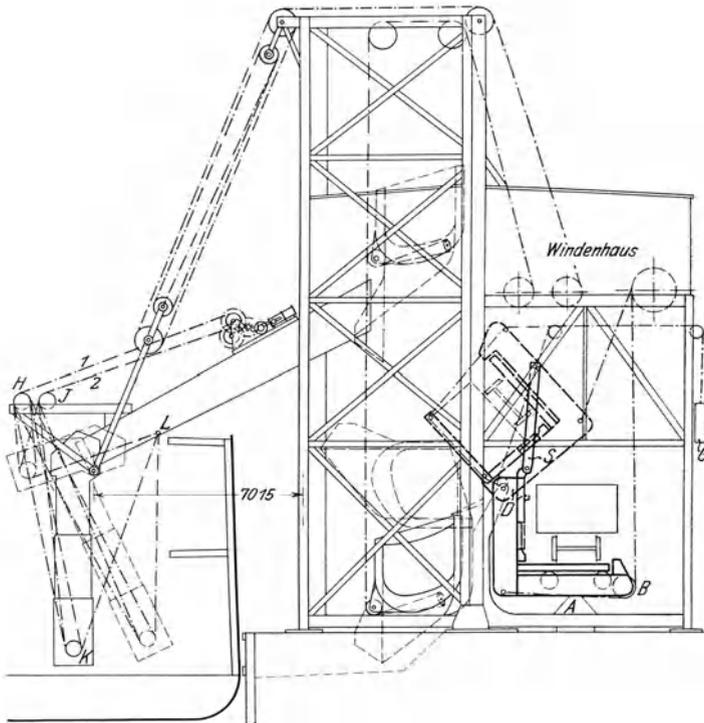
Amerikanischer Seitenkipper für zerbrechliche Kohle mit besonderer Hebevorrichtung. Mac Myler Mfg. Co.
